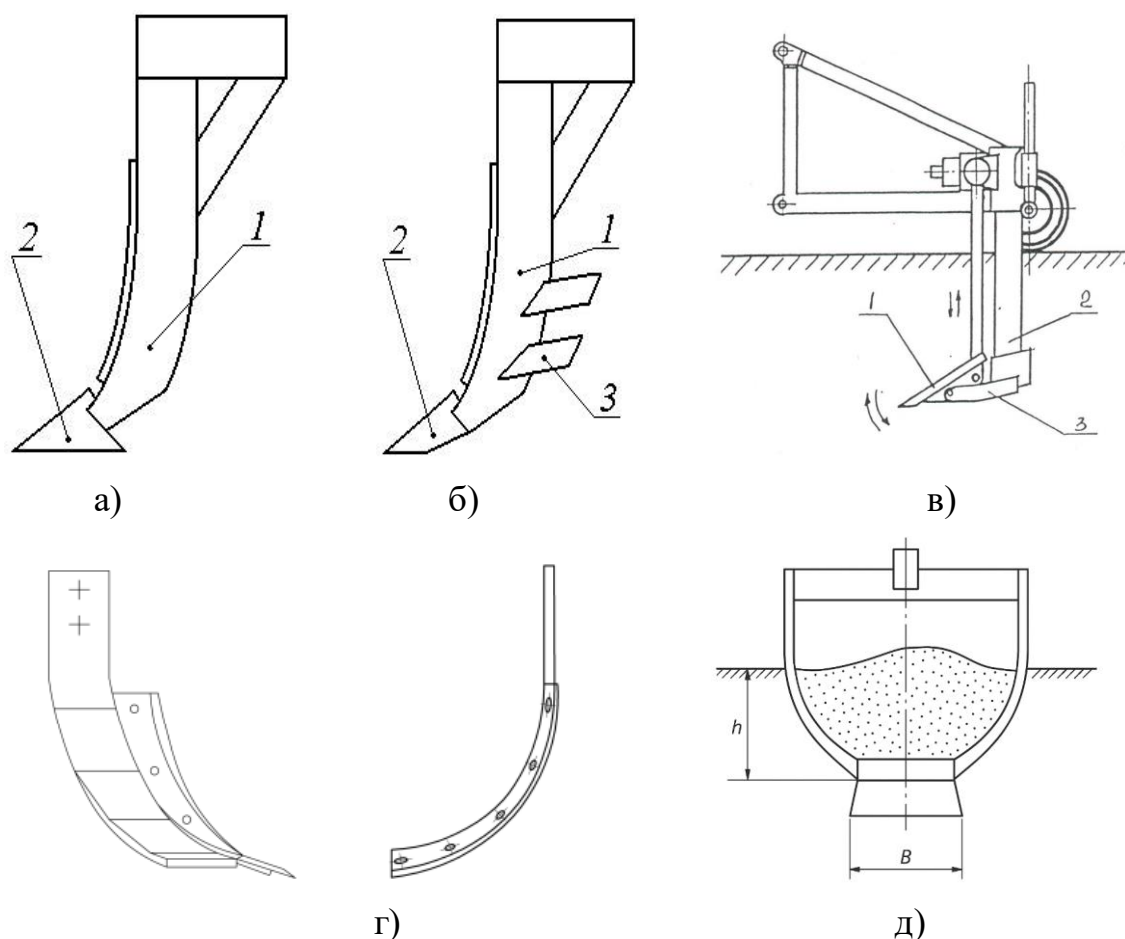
Різновиди конструкцій робочих органів глибокорозпушувачів:
